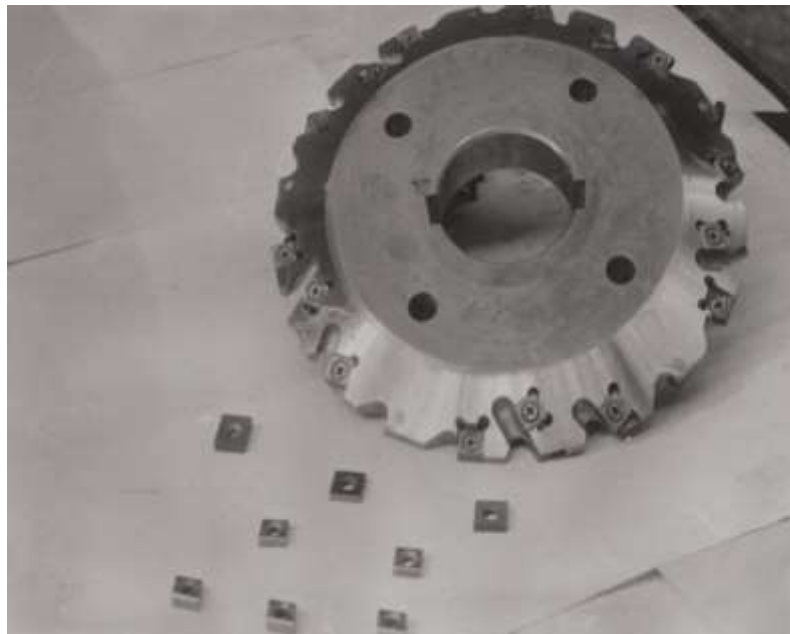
Дискова зуборізна фреза з механічним кріпленням багатогранних твердосплавних пластин [26]
